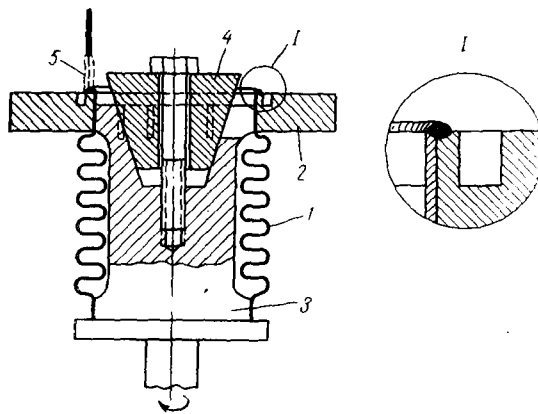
Сварка сильфона с фланцем:
